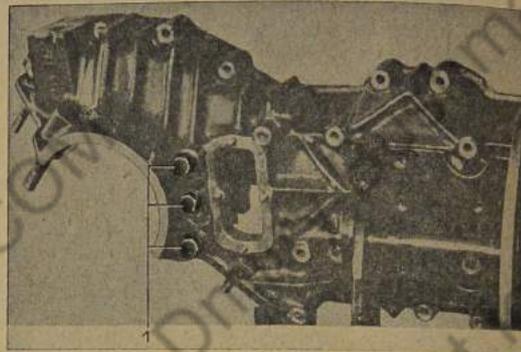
Lagerbock für Zylinderrollenlager des Antriebskegelrades anschrauben
